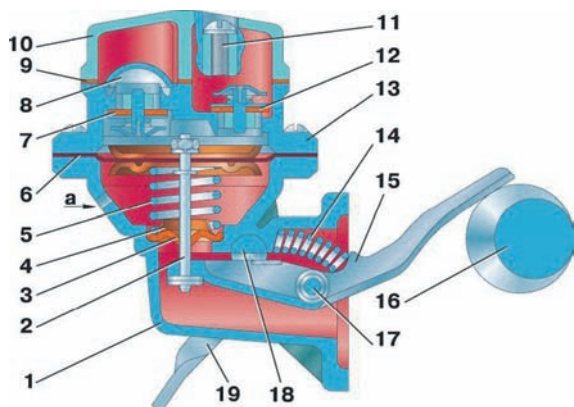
Паливний насос Б9В (451М-1106010-30, 451М-1106010-30): а - контрольний отвір; 1 - корпус; 2 - шток; 3 - ущільнювач; 4 - шайба; 5, 14 - пружини; 6 - діафрагма; 7 - впускний клапан; 8 - фільтр-сітка; 9 - прокладка; 10 - кришка; 11 - гвинт; 12 - випускний клапан; 13 - головка корпусу; 15 - важіль приводу; 16 - эксцентрик розподільного вала; 17 - вісь важеля приводу; 18 - валик важеля ручної підкачки; 19 - важіль ручної підкачки
